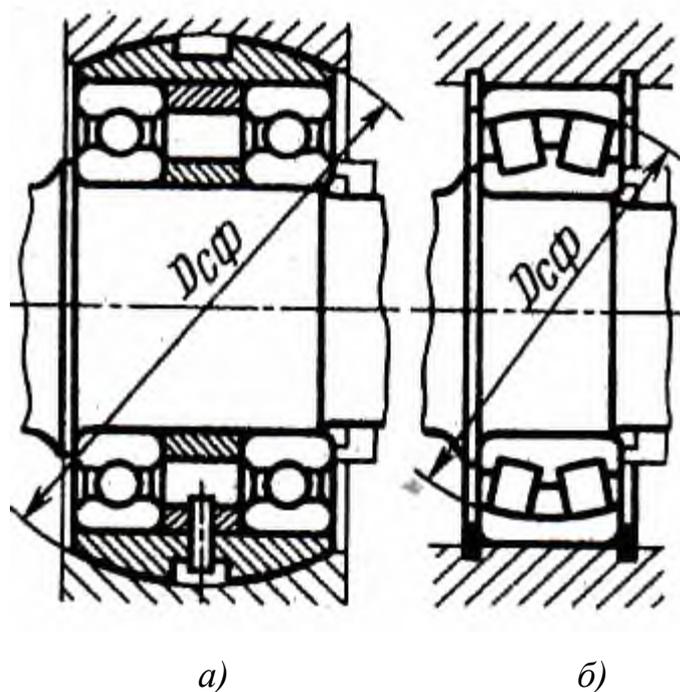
Обеспечение самоустанавливаемости подшипников качения
